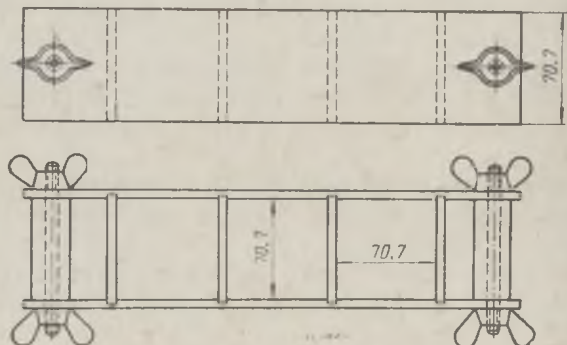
Форма для изготовления из растворной смеси образцов-кубов (без дна)
